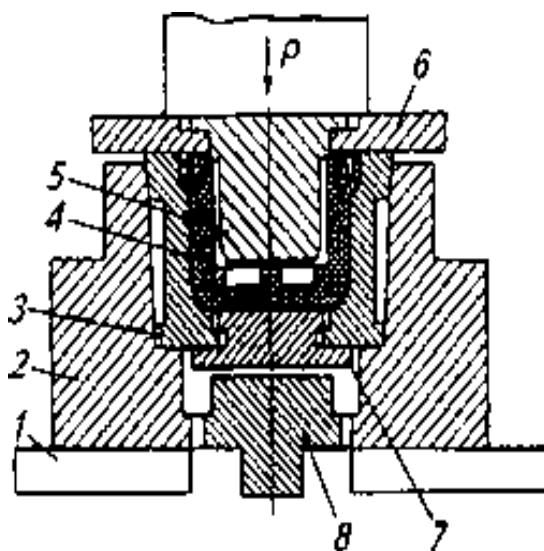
Схема обтиску корпусу насоса типу НШ на пресі:
